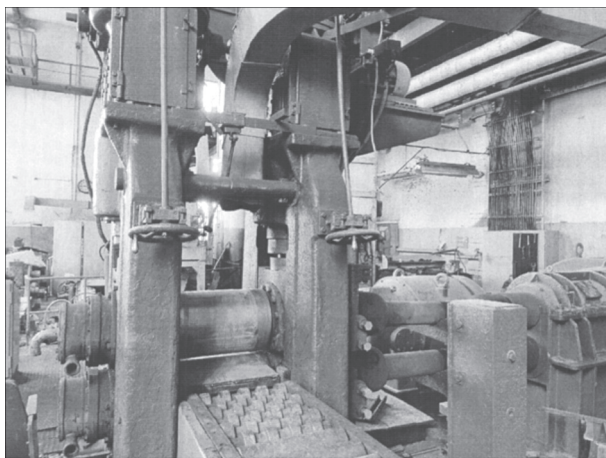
Лабораторний реверсивний прокатний стан «Skoda 355/500»
